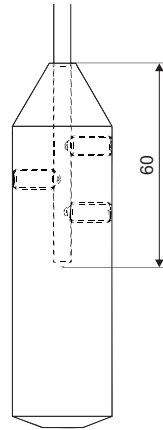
Zeichnung des Gewichtes der Seilelektrode
